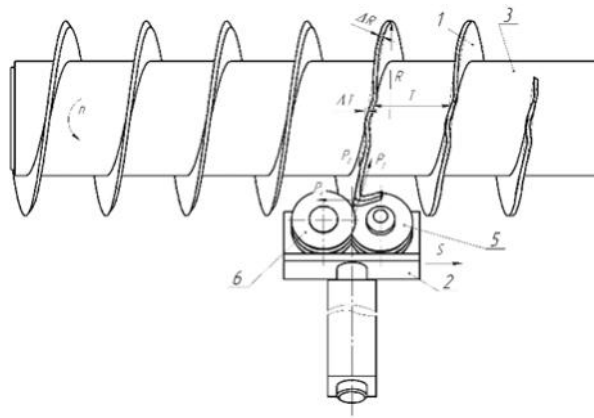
Схема розташування похибок попередньо сформованої гвинтової заготовки методом навивання на оправу та розтягу на крок: 1 – заготовка гвинтового елемента; 2 – ріжучий інструмент; 3 – затискний елемент; 4 – оправка; 5 – ріжуча пластина для заточування крайки гвинтового елемента; 6 – ріжуча пластина для запобігання формуванню заусенців
